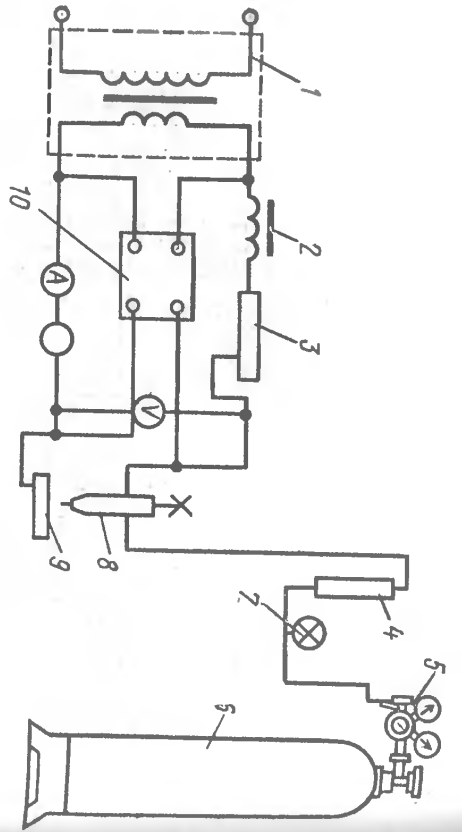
Схема сварки в инертных газах на переменном токе: 1 — сварочный трансформатор, 2 — дроссель, 3 — балластный реостат, 4 — релактор, 5 — редуктор, 6 — баллон с газом, 7 — манометр, 8 — сварочная горелка, 9 — свариваемая заготовка, 10 — осциллограф ОС-1
